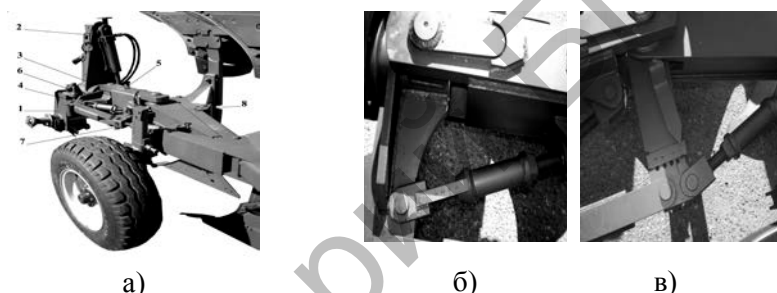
Механизм поворота рамы и изменения ширины захвата плуга
